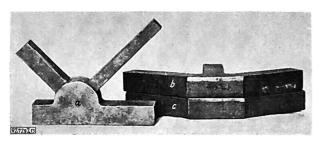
K-Stück a Form des Versuchstückes b Bruchprobe von Grauguß mit Lunker c " Perlitguß ohne "
